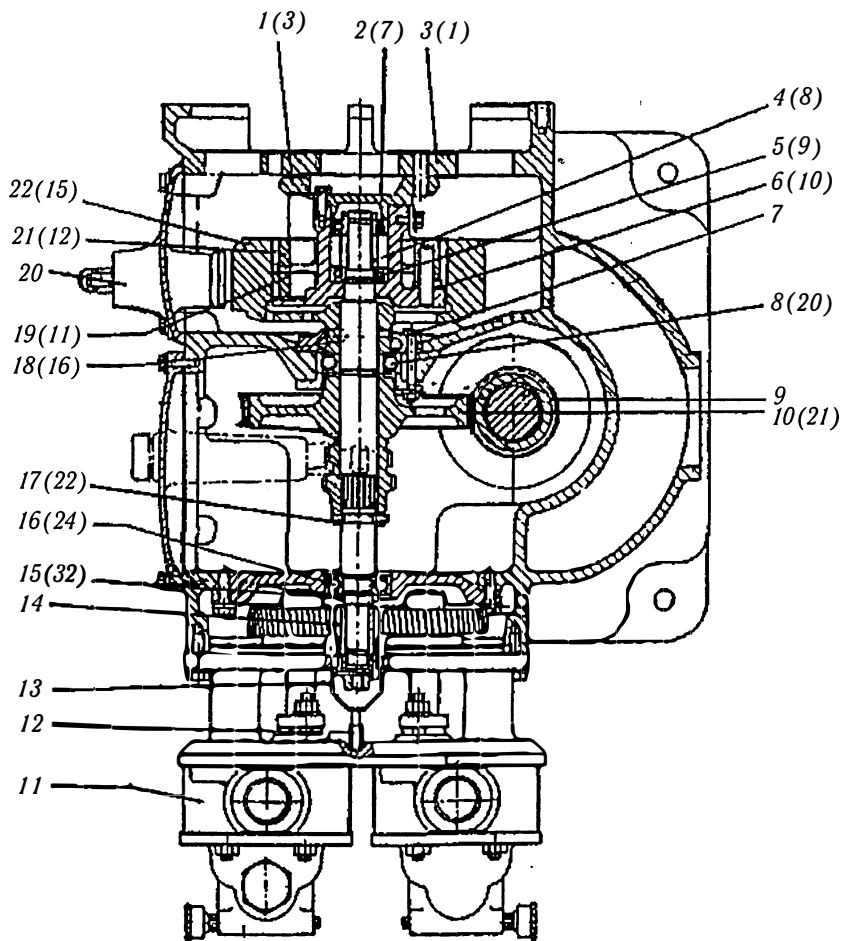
Горизонтальный вал в сборе: 1 — поводок; 2 — подшипник фрикционной муфты; 3 — резиновая эластичная муфта; 4 — распорная втулка; 5 — подшипник фрикционной муфты; 6 — корпус фрикционной муфты; 7 — болт; 8 — шарикоподшипник червячного колеса; 9 — червяк; 10 — червячное колесо; 11 — шестеренный насос; 12 — предохранительный клапан; 13 — колпак защитный; 14 — ведущая шестерня насоса; 15 — крепежная гайка подшипника; 16 — шарикоподшипник; 17 — стопорная гайка; 18 — горизонтальный вал; 19 — колодка фрикционной муфты; 20 — тормоз; 21 — накладка фрикционной колодки; 22 — обод фрикционной муфты
